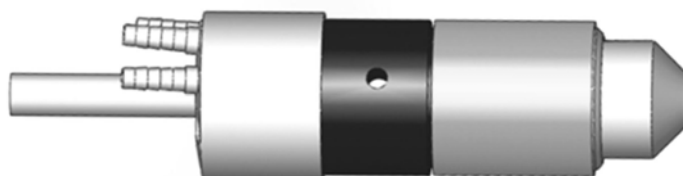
Сварочный плазмотрон (CAD-модель)
